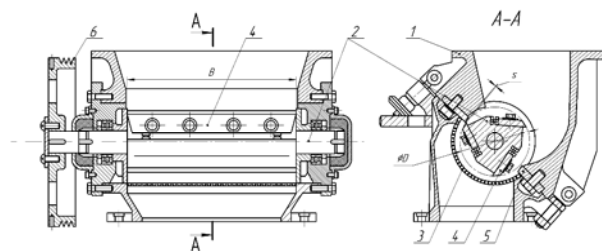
Схема дробарки для подрібнення пластмас: 1 – корпус; 2 – ротор; 3 – ситко; 4 – ніж ротора; 5 – нерухомий ніж; 6 – шків
